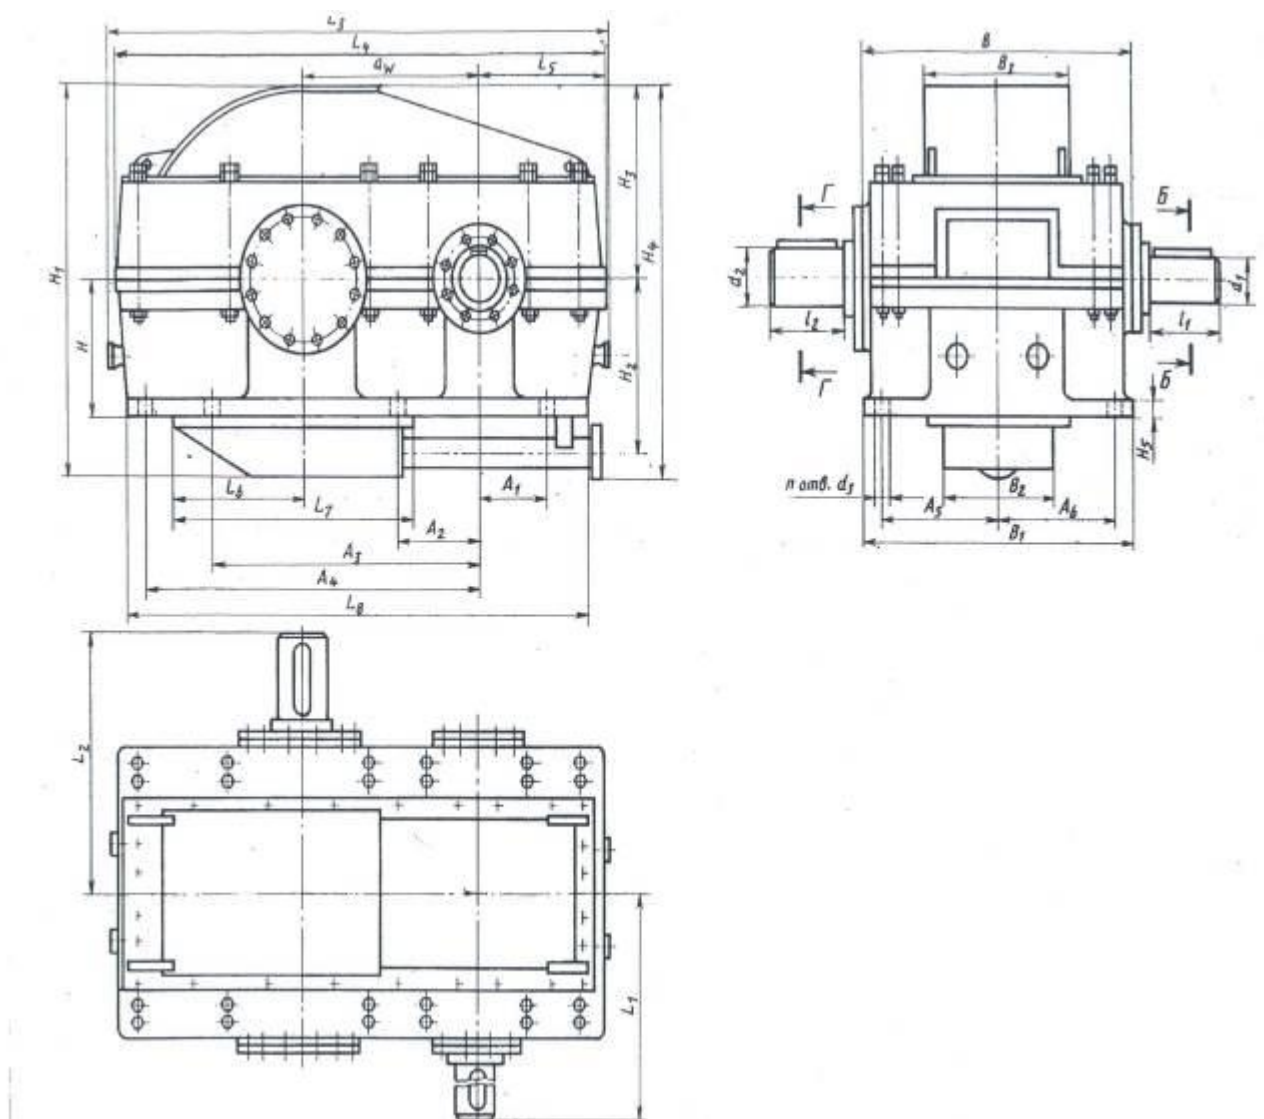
Габаритные и присоединительные размеры цилиндрического редуктора
